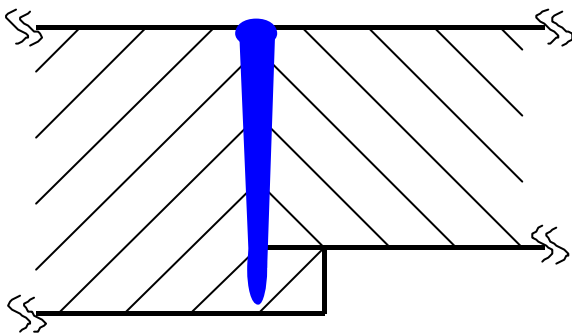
Geometrische Konfiguration der Nahtausführung mit einer schematisch eingezeichneten Einschweißung.
